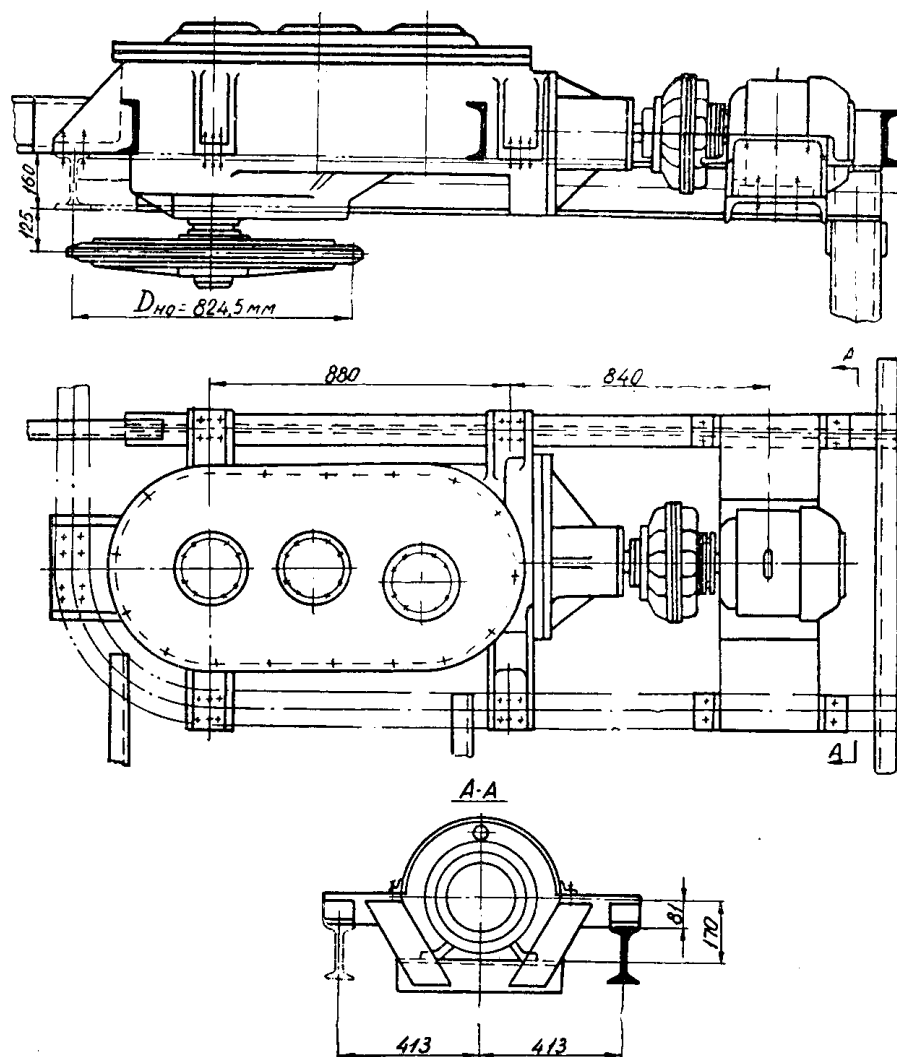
Общий вид одной из приводных станций двухдвигательного подвесного конвейера с предохранительными турбомуфтами
